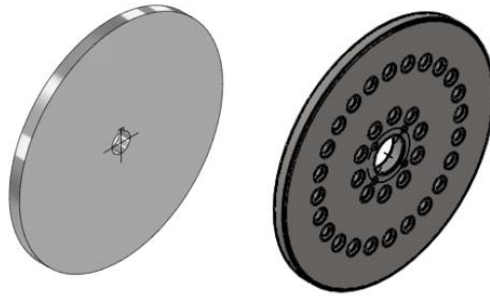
Vista isométrica del disco móvil o disco rotatorio. Izq: diseño anterior [1], Der: diseño actual.
